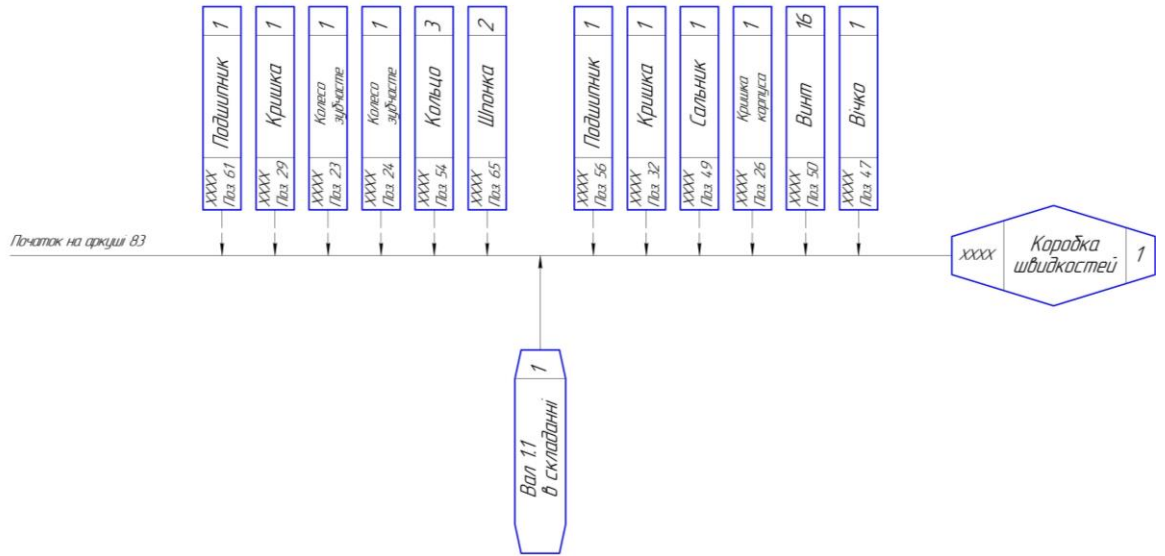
Технологічна схема складання коробки швидкостей зубофрезерного верстата 5К32 (частина 4).
